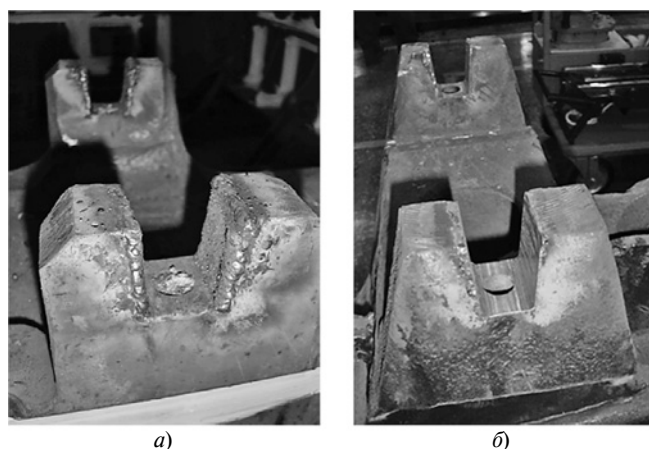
Вид изношенного паза, наплавленного сварным электродом (а), и паза после фрезерования (б)
